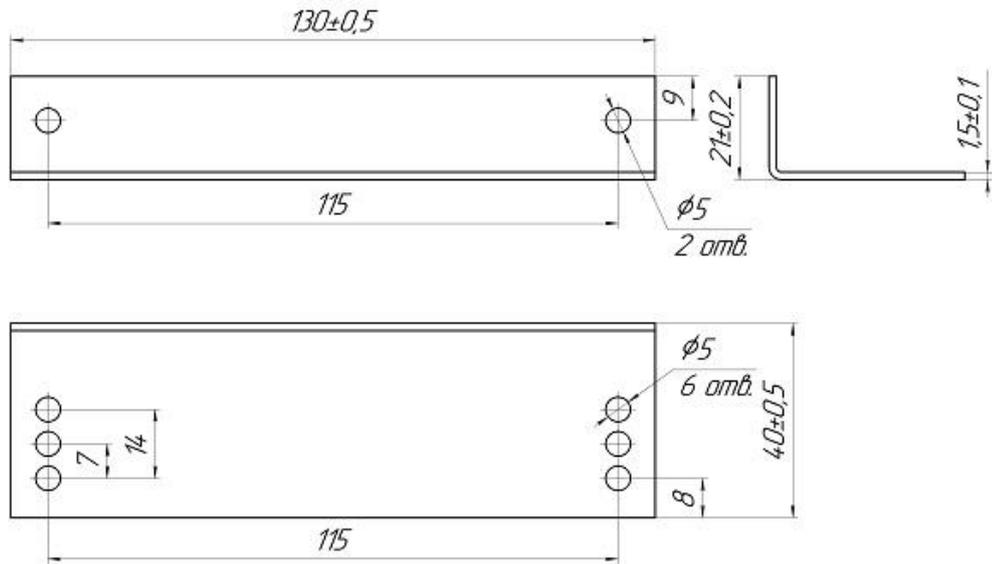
Габаритные и присоединительные размеры кронштейна К-26 АЯКС
